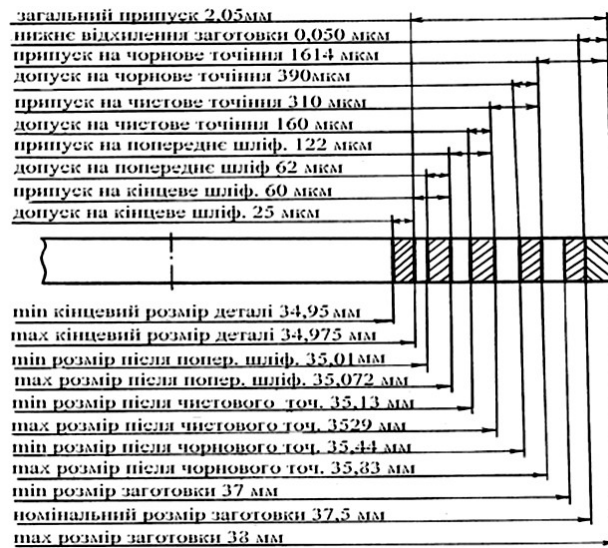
Схема припусків і допусків на обробку
